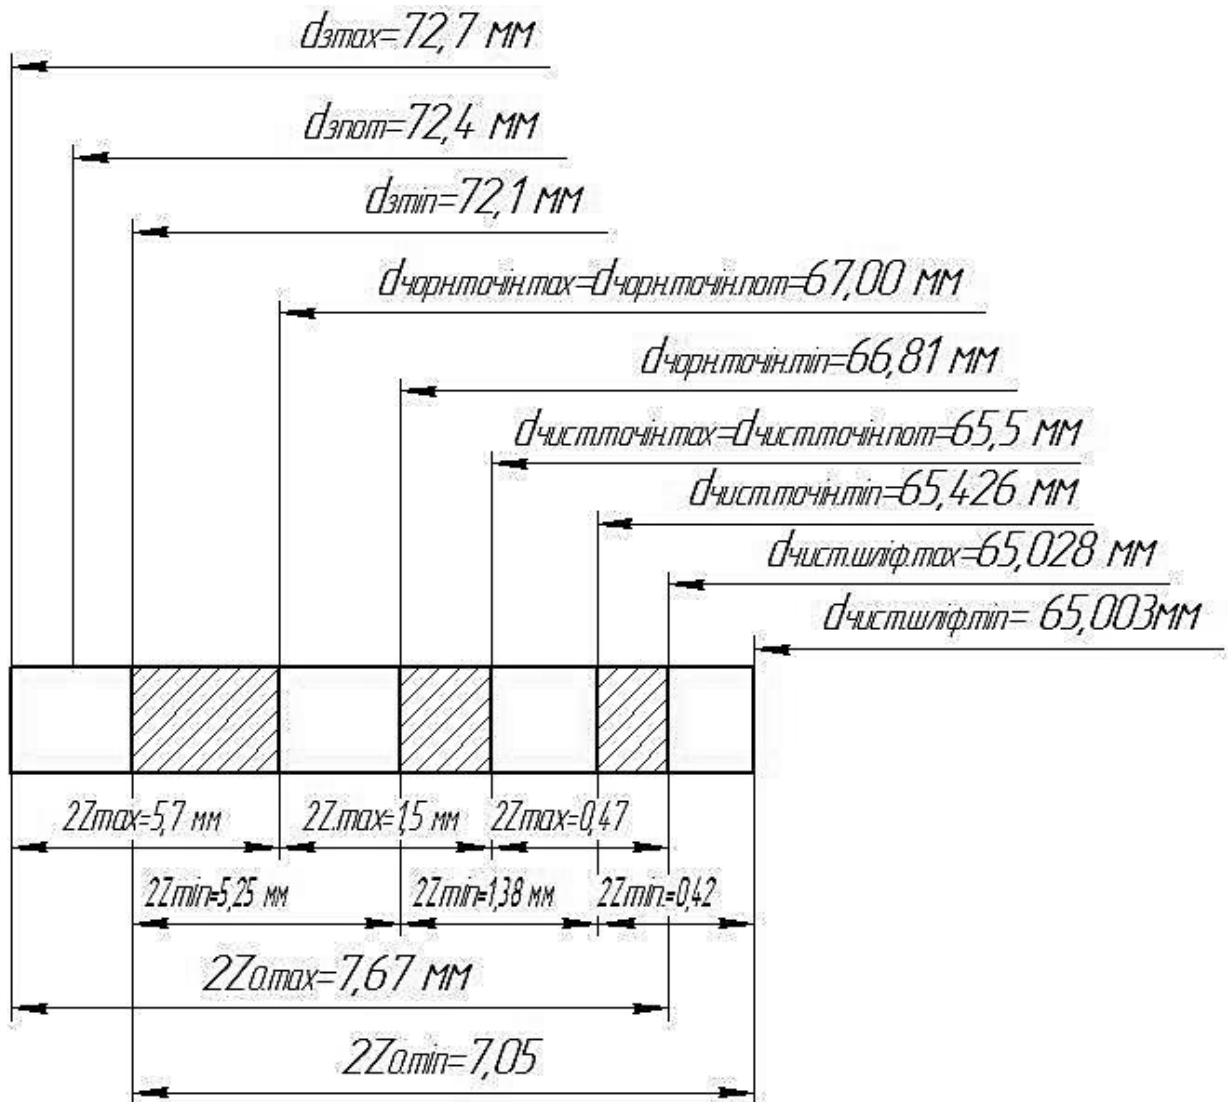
Схема розташування полів допусків і припусків на обробку поверхні
